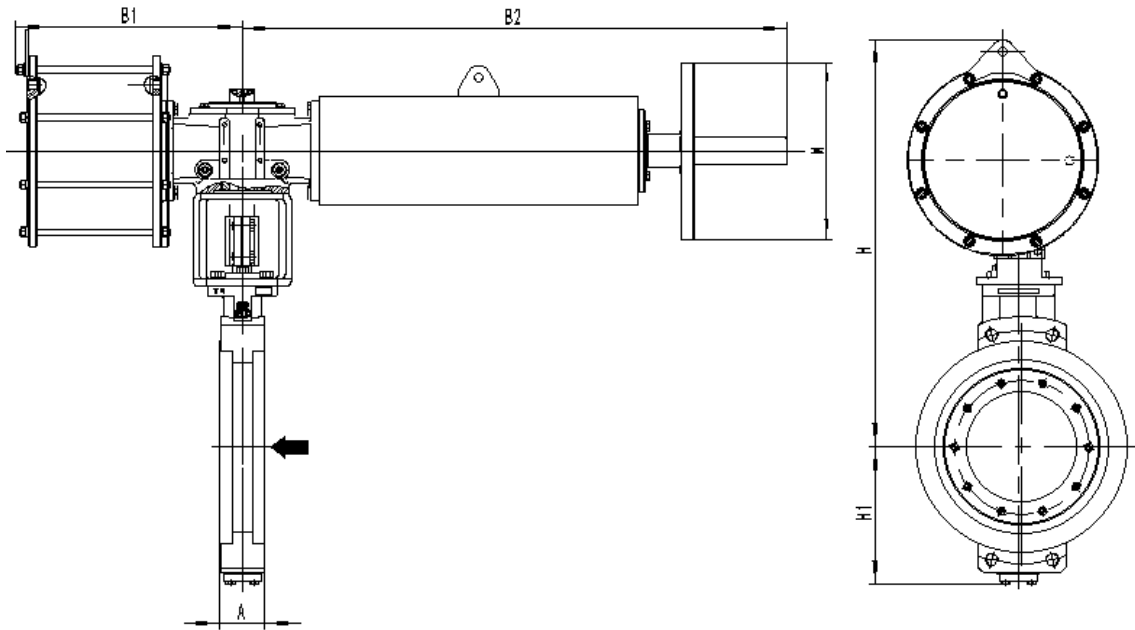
配 AW18SR41~AW27SR52 带丝杆手轮外形尺寸图 (FC)
